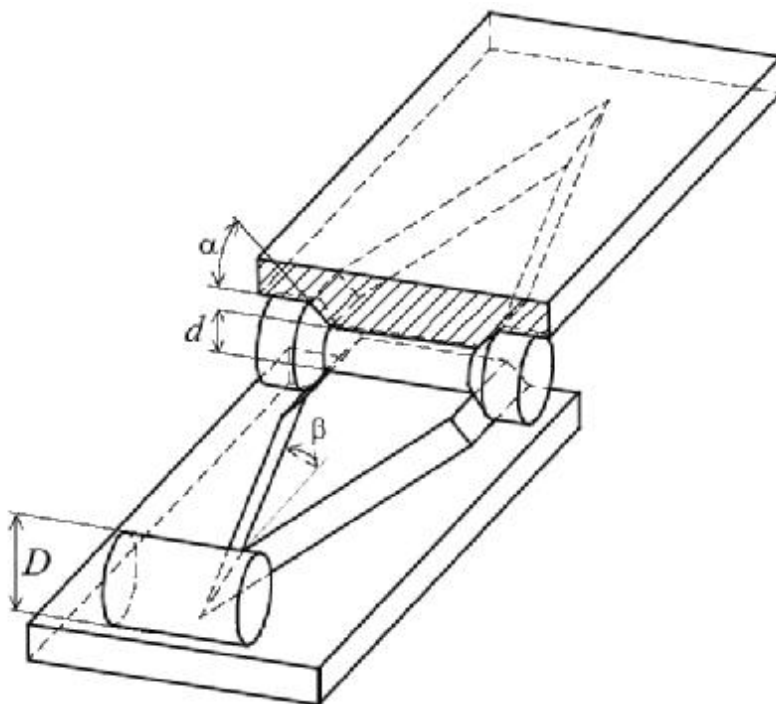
Схема плоского клинового інструменту ППКП та його конструктивно-технологічні параметри: α – кут нахилу бічної грані; β – кут загострення; D – діаметр заготовки; d – діаметр прокатаного ступеня заготовки
